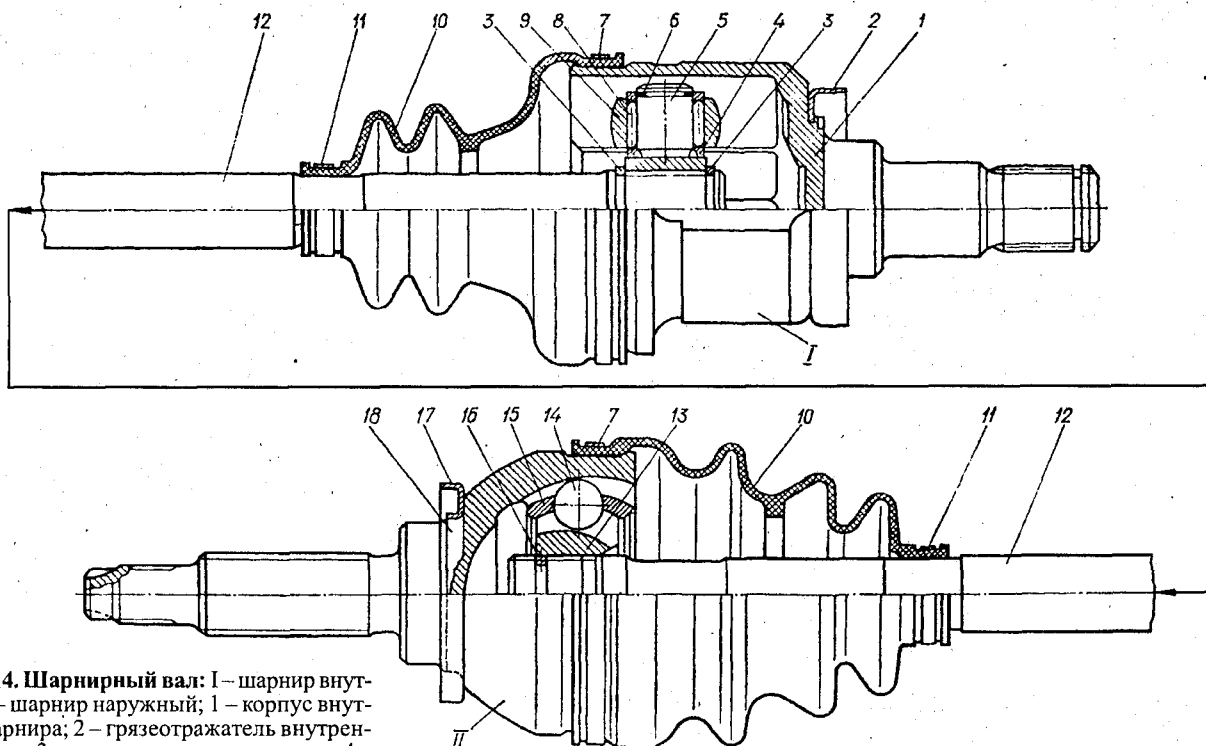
Шарнирный вал: I – шарнир внутренний; II – шарнир наружный; 1 – корпус внутреннего шарнира; 2 – грязеотражатель внутреннего шарнира; 3 – кольцо стопорное плоское; 4 – шайба запорная игольчатого подшипника; 5 – трехшиповик; 6 – кольцо стопорное запорной шайбы; 7 – хомут большой; 8 – иголка подшипника; 9 – ролик; 10 – чехол; 11 – хомут малый; 12 – вал шарниров; 13 – обойма внутренняя; 14 – шарик; 15 – сепаратор; 16 – кольцо стопорное; 17 – грязеотражатель наружного шарнира; 18 – корпус наружного шарнира
